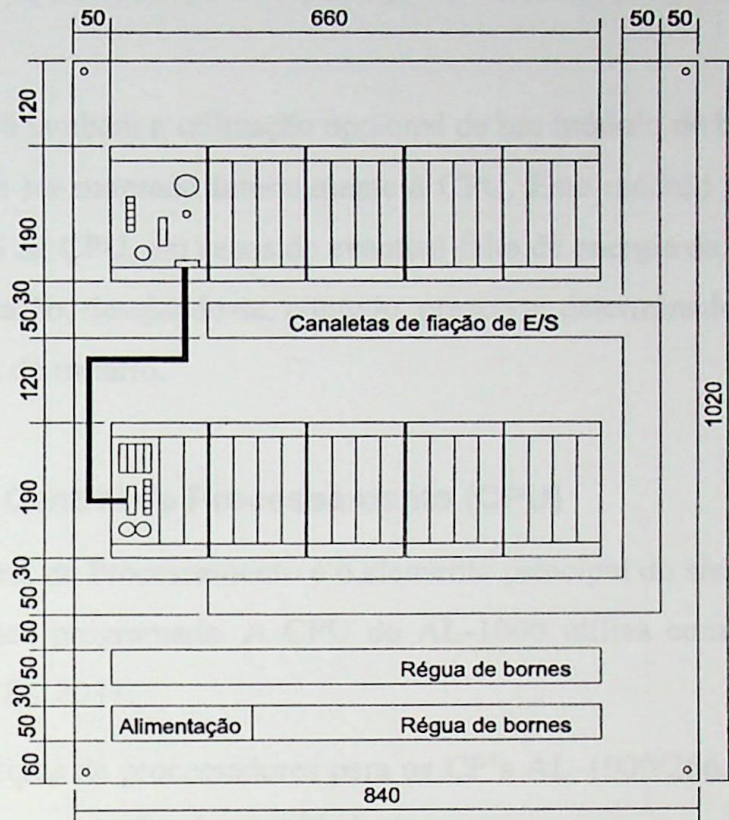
Dimensões da placa de montagem para sistema de 256 pontos
